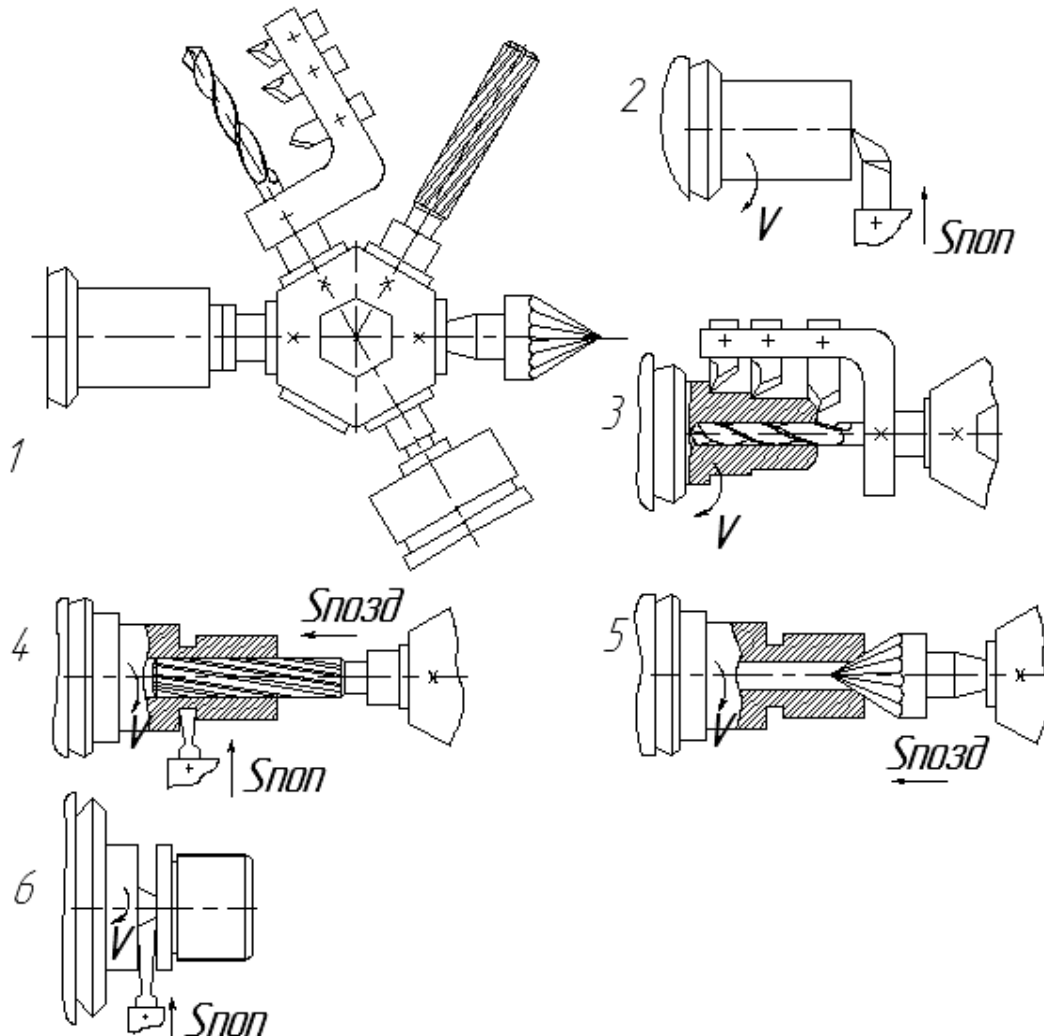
Схеми обробки поверхонь заготовок на токарно-револьверних верстатах
